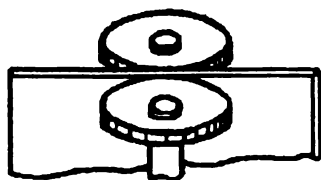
Продвигатель тканей с двумя рифлеными рейками
